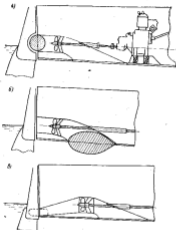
Установка водометного двигателя в корпусе катамарана: а — полуподводный выброс струи; б — устройство заглушки на входном отверстии; в — подводный подводный выброс струи.
